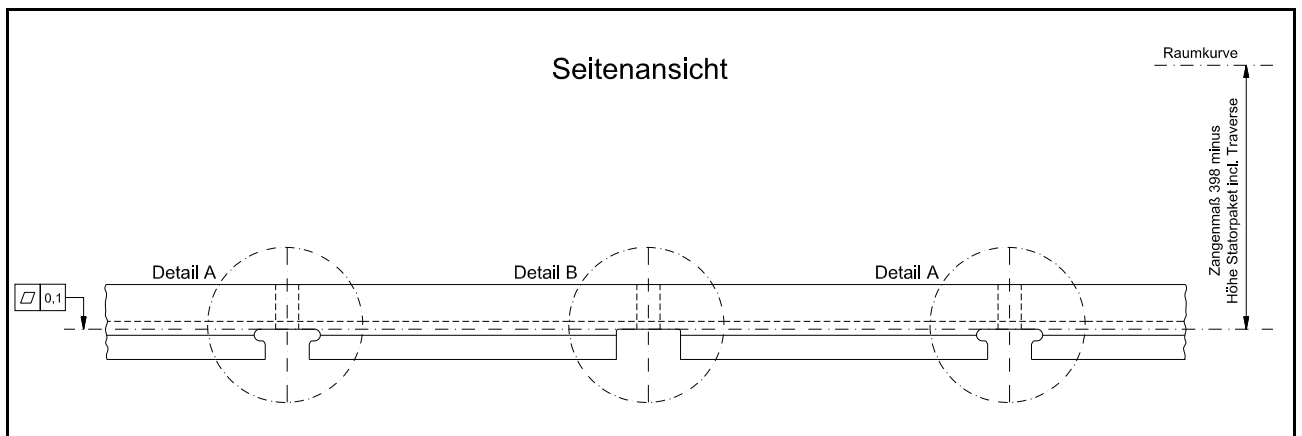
Maße und Toleranzen für die Ausführung der Statorpaketaufnahme in Stahlbauweise (Seitenansicht)
